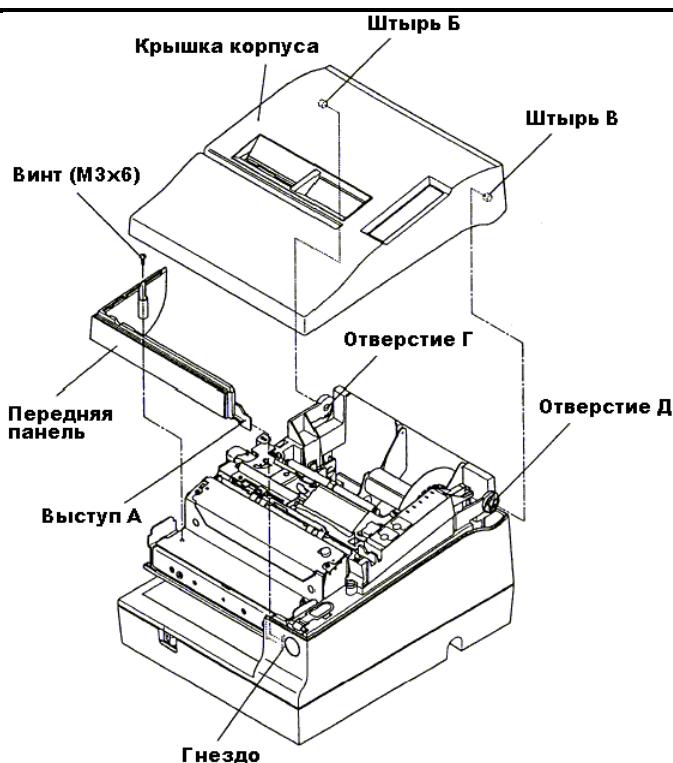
Отсоединение крышки корпуса и лицевой панели
